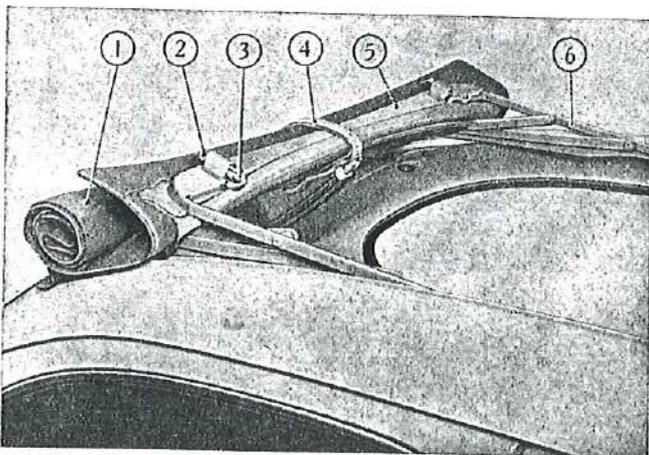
Detalle de la fijación del techo rebatible, con capota plegada.
